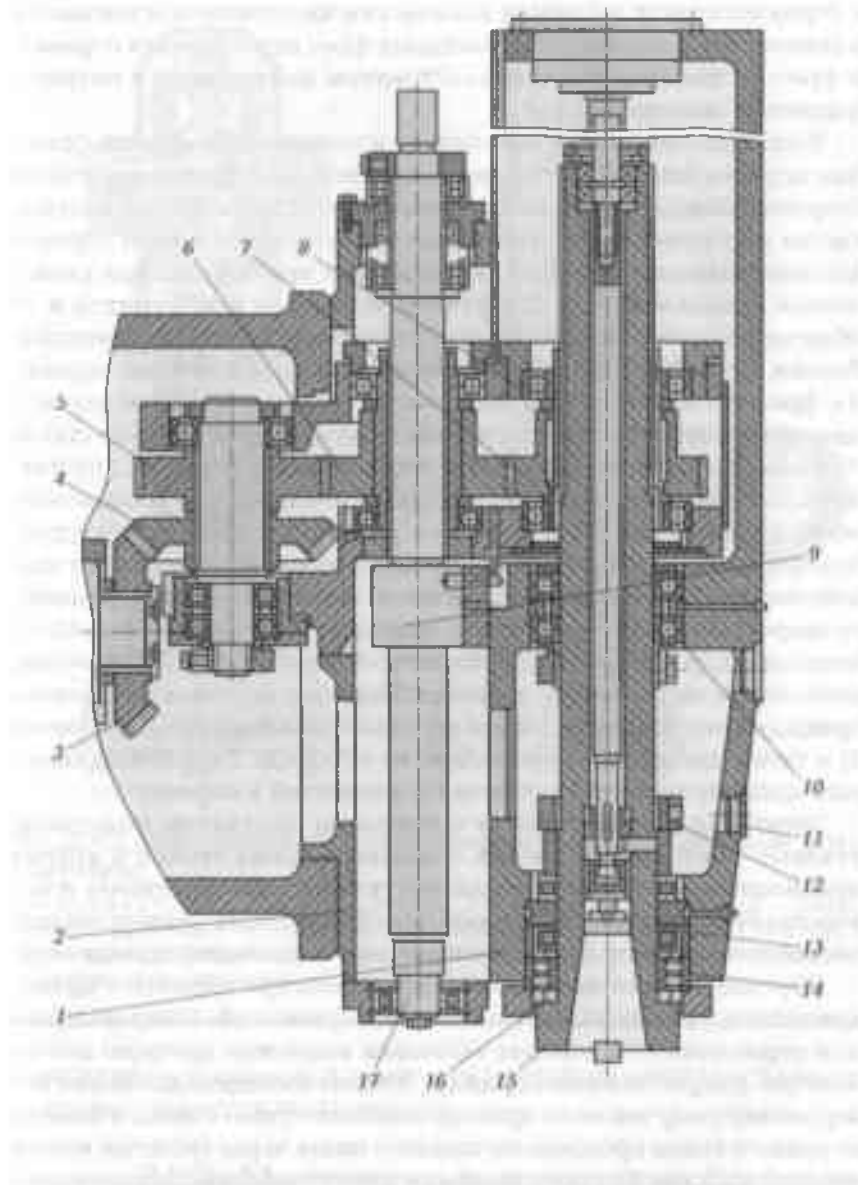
Шпиндельная бабка с ползуном вертикально-фрезерного станка с числовым программным управлением:
